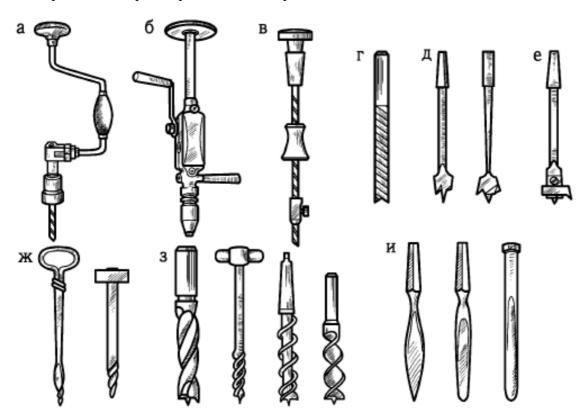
Инструмент для сверления: a – коловорот;  $\delta$  – ручная дрель; e – сверлилка; e – спиральное сверло;  $\partial$  – перовые сверла; e – универсальное сверло; m – буравы; e – винтовые сверла; e – ложечные сверла
